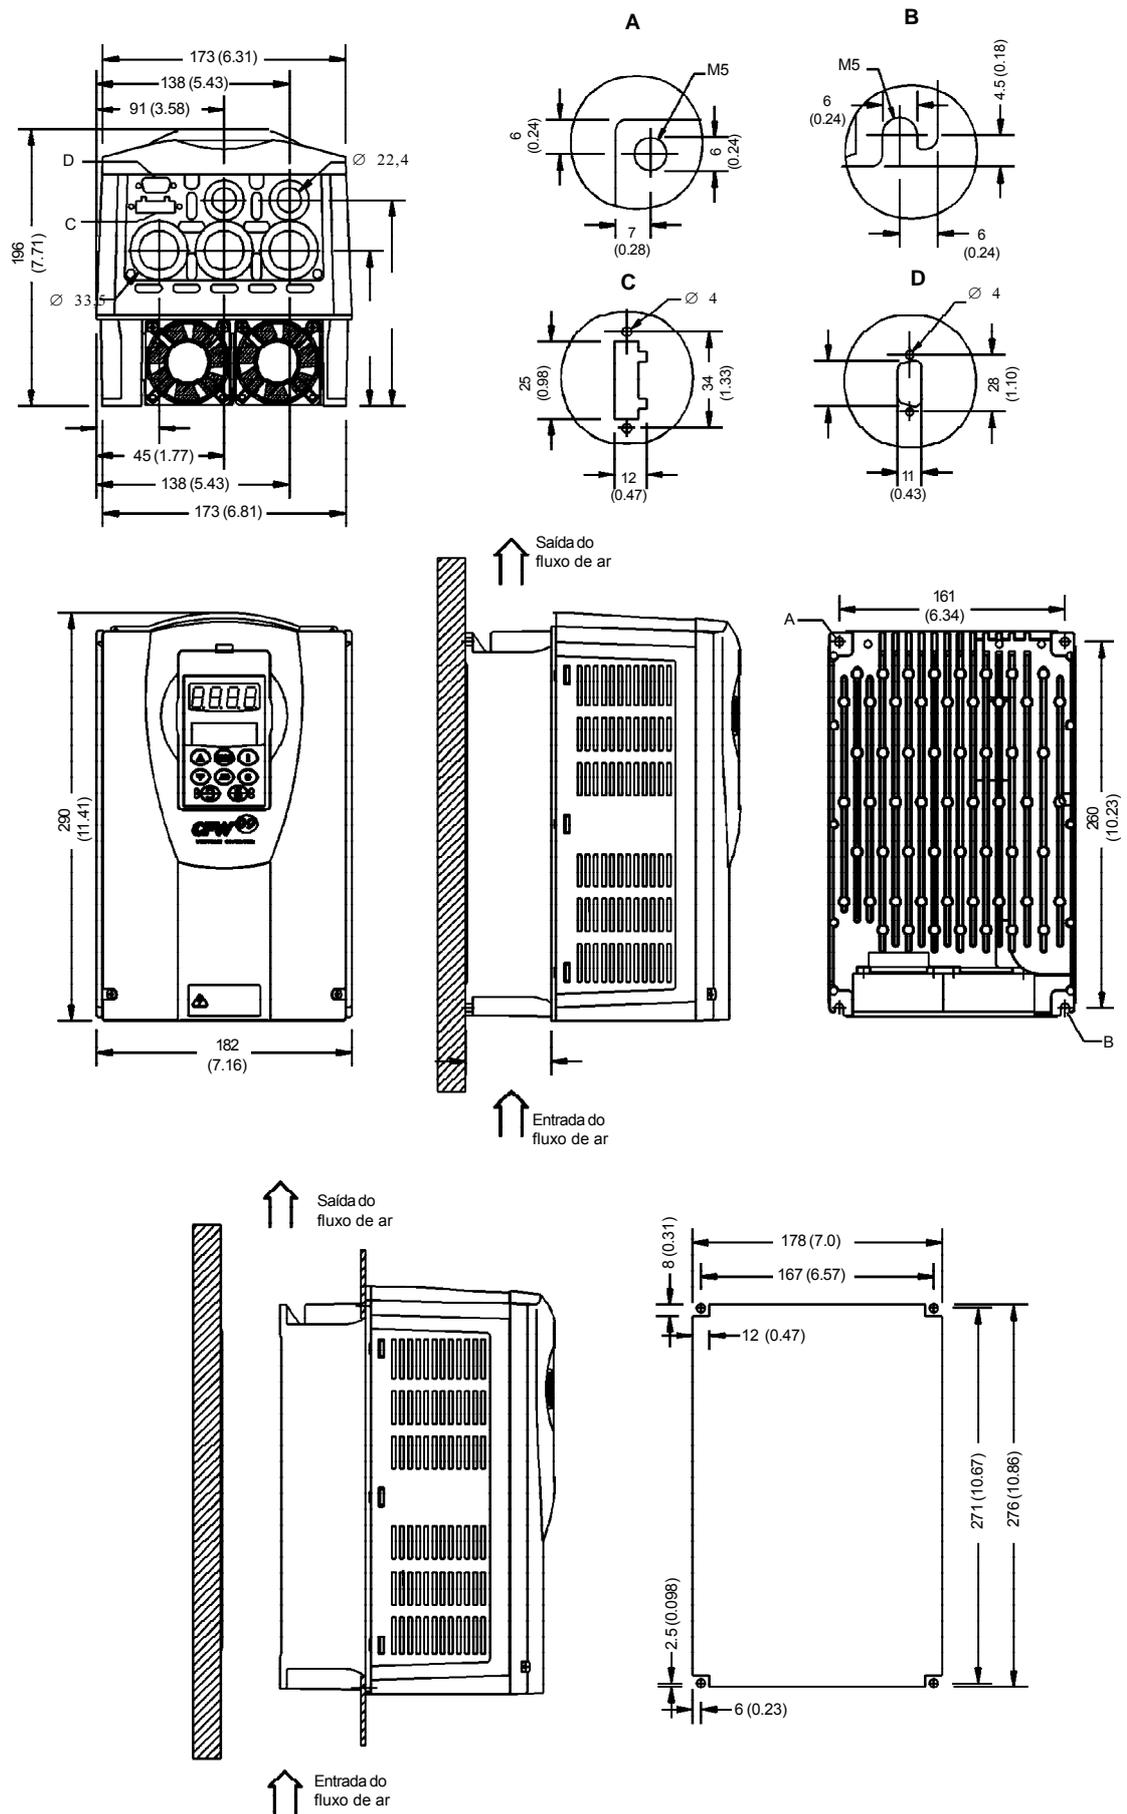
Mecânica 2 - Dimensões em mm (polegadas)
